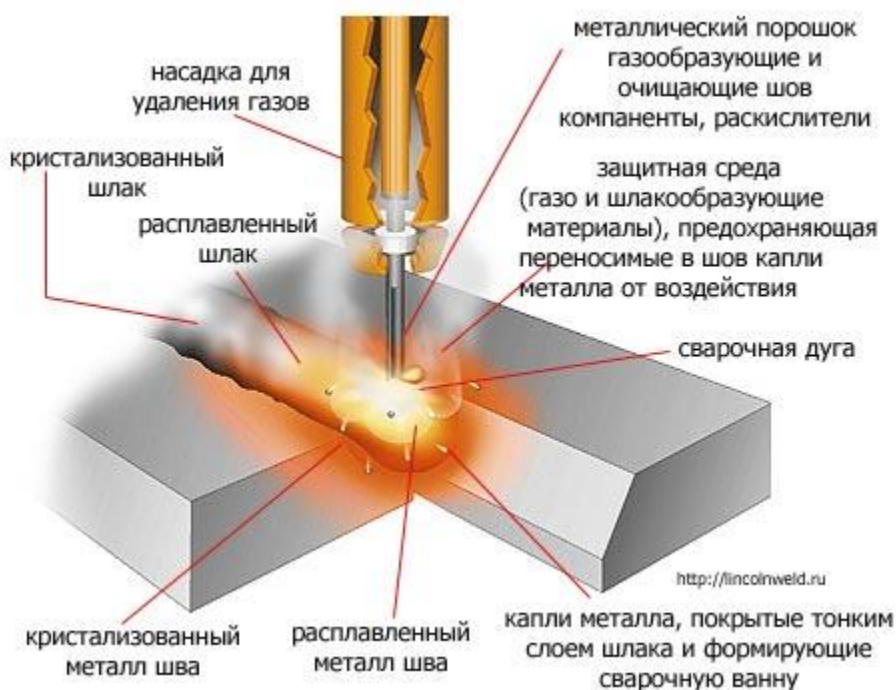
Схема процесса сварки самозащитной порошковой проволокой
